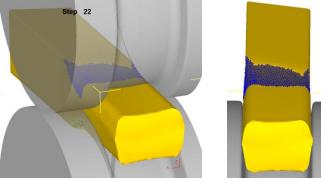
Точки контакта заготовки с поверхностью валка на стадии установившегося процесса прокатки заготовки с величиной ромбичности 20 мм и начальным углом поворота заготовки 6°
